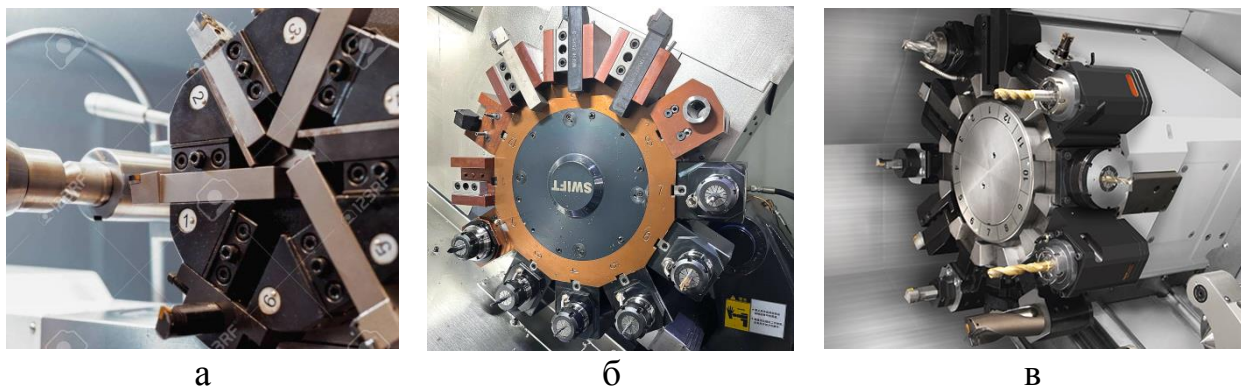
Інструментальні магазини токарних верстатів з ЧПК: а – різцетримач на шість позицій; б, в – револьверна головка на 12 позицій
